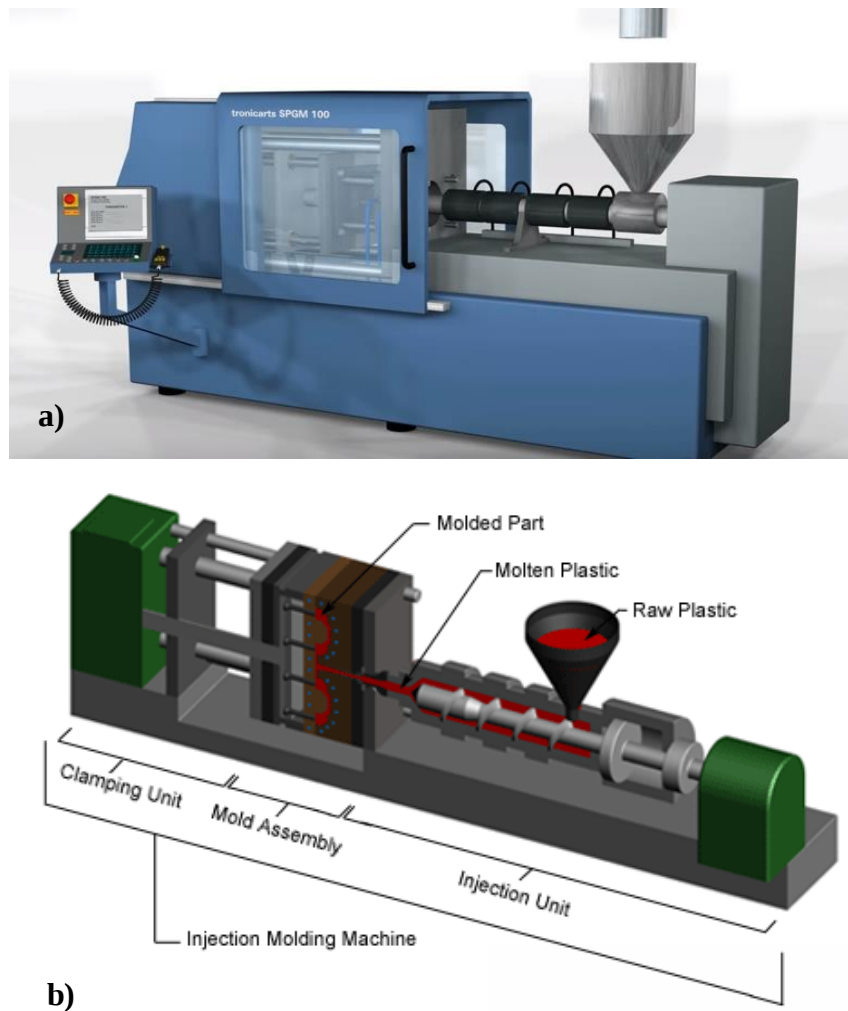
a) Máquina injetora; b) Interior da máquina injetora - Processo de moldação por injeção [Adaptado de (CustomPartNet)].
